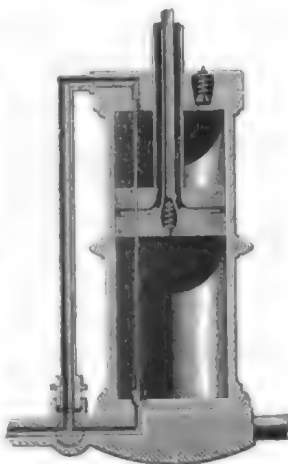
Corps de pompe de la machine de M. Bianchi.
